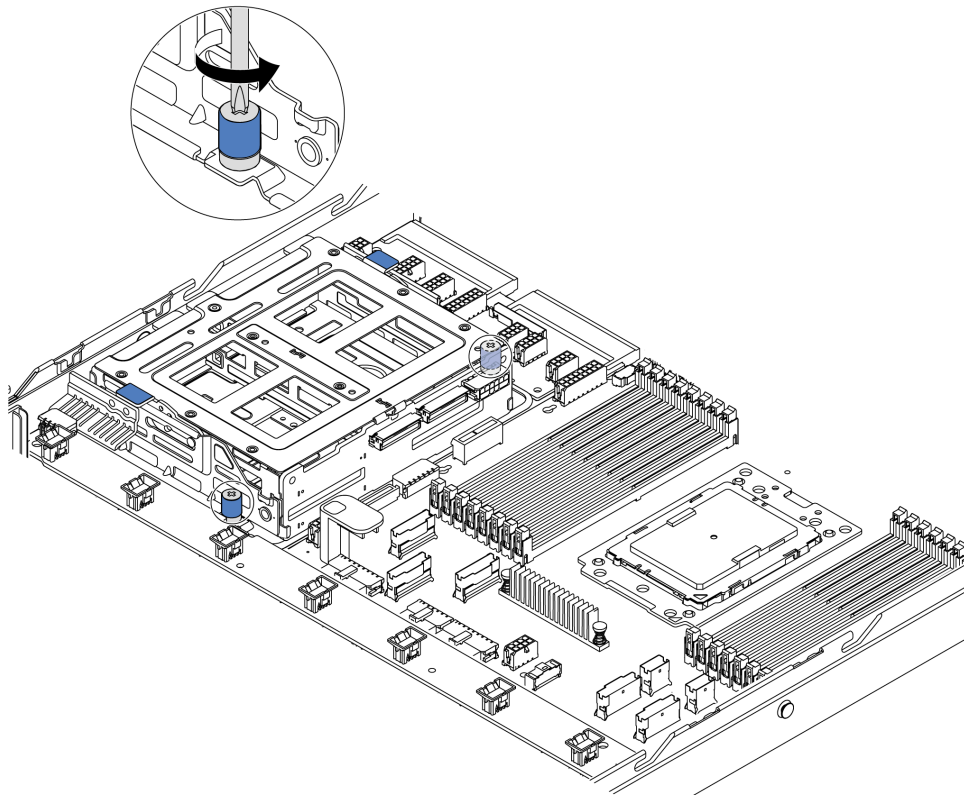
Entfernen der mittleren Laufwerkhalterung 1
